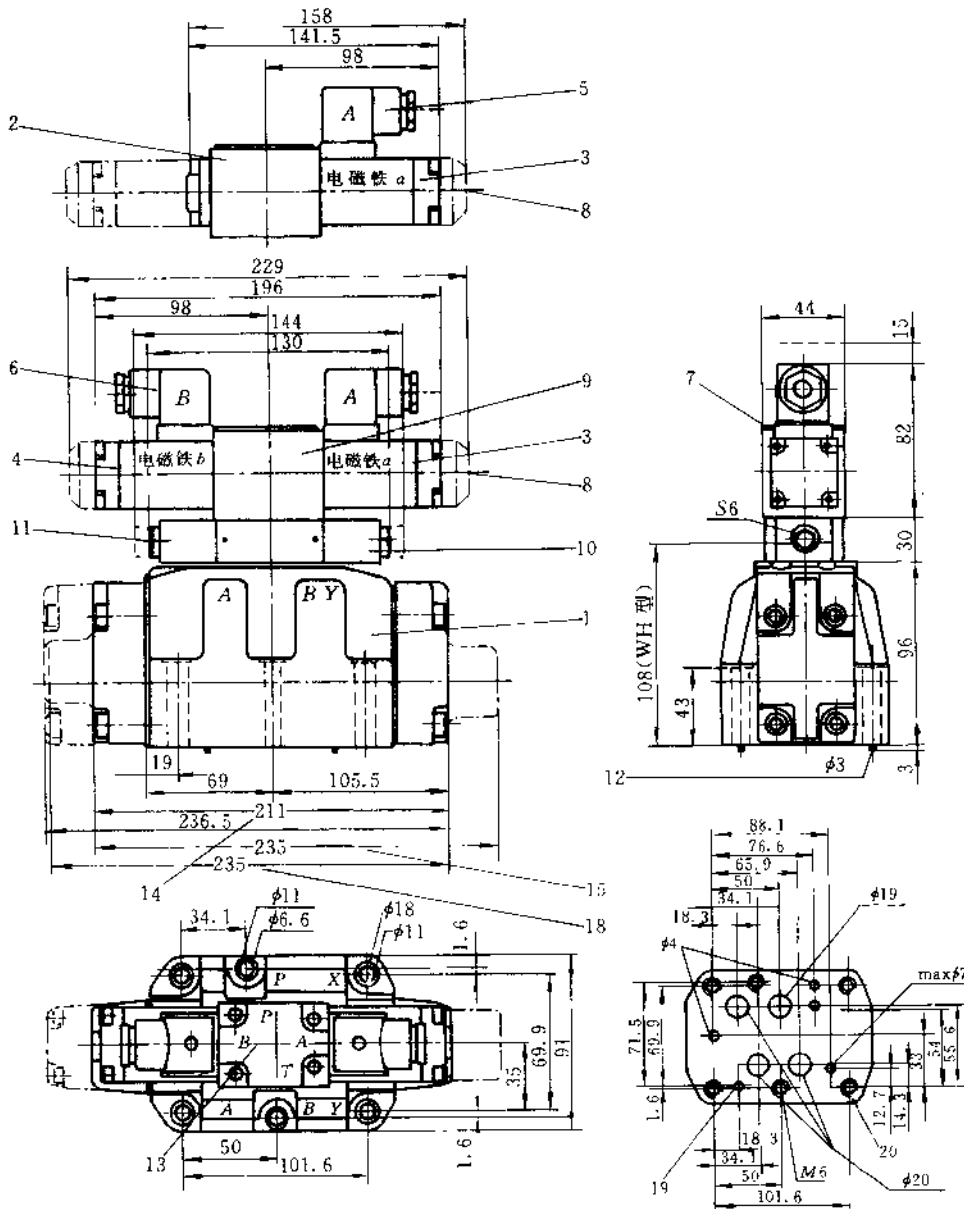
WEH/WH16 型换向阀外形连接尺寸图
